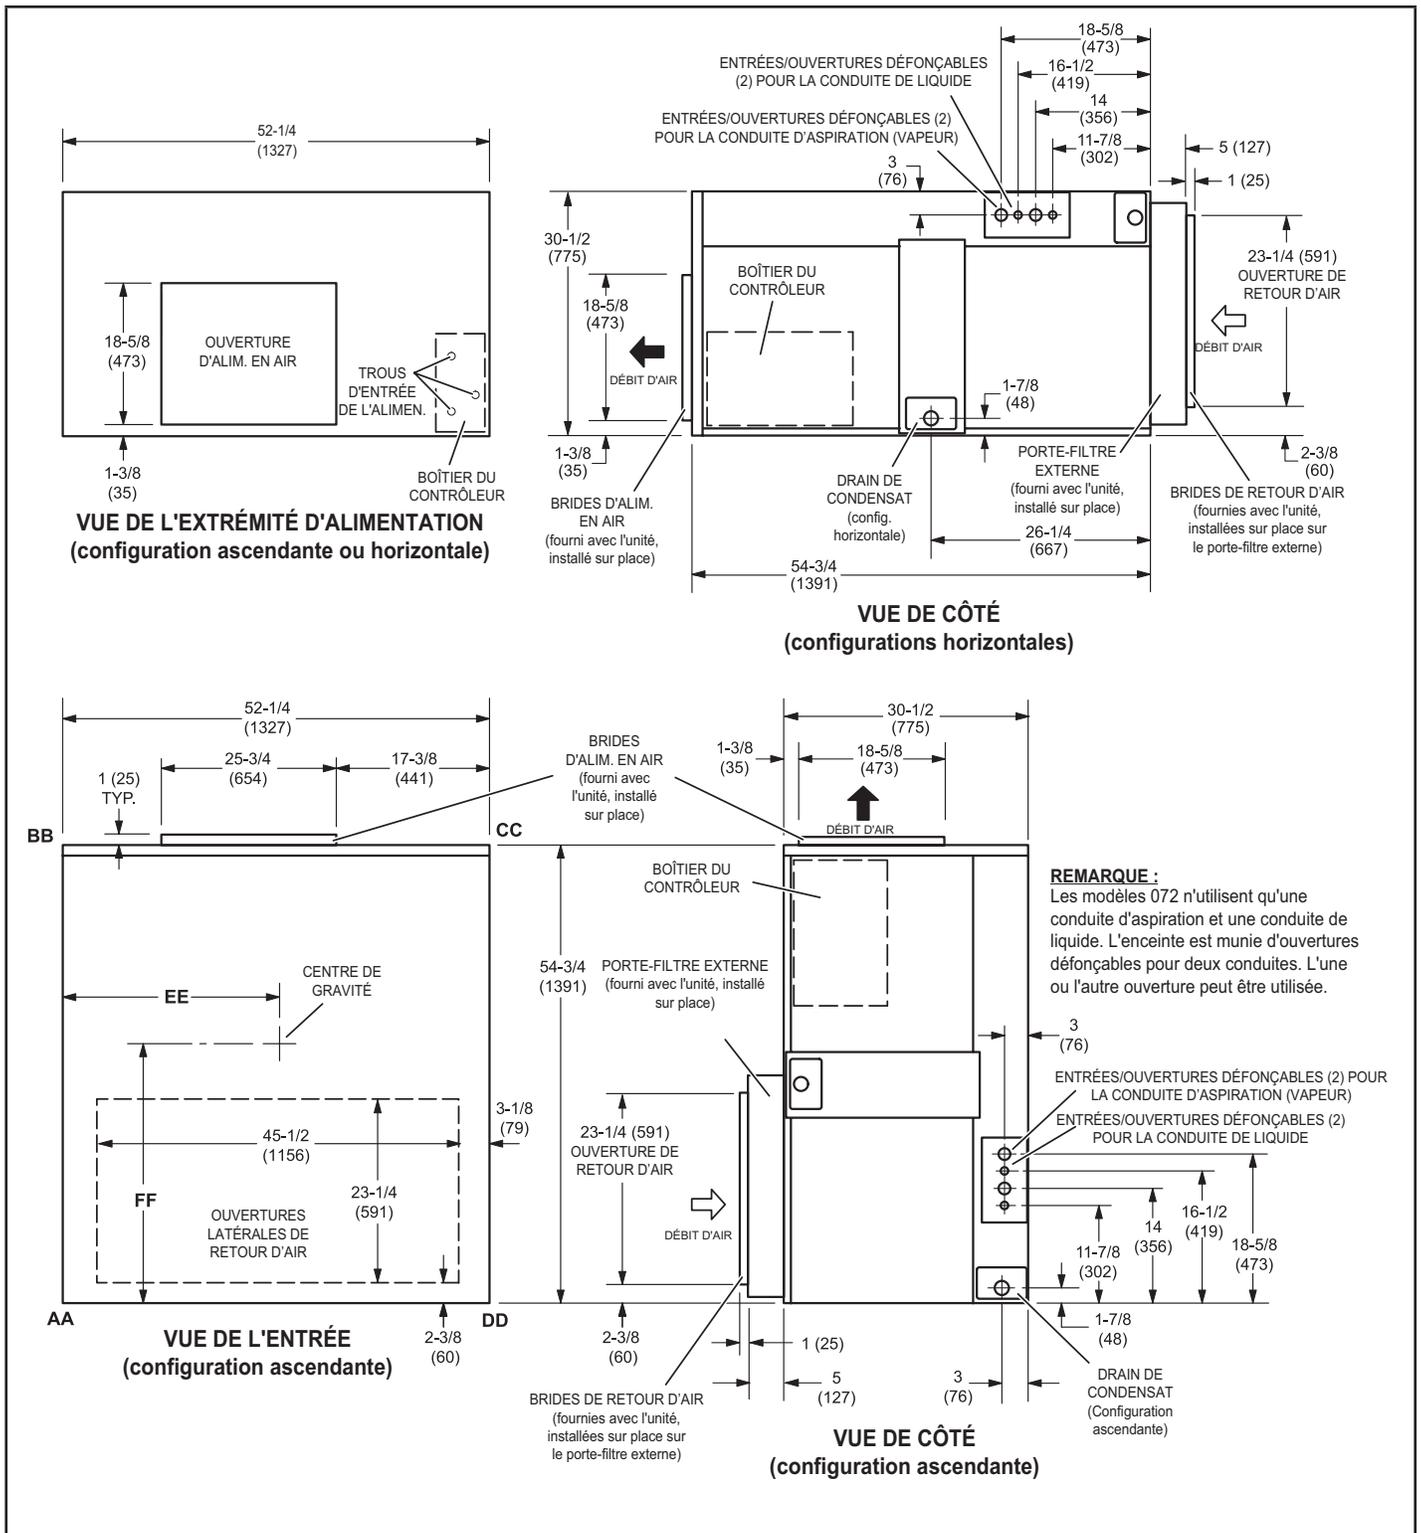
Dimensions de l'unité EL072-090KA – pouces (mm)
